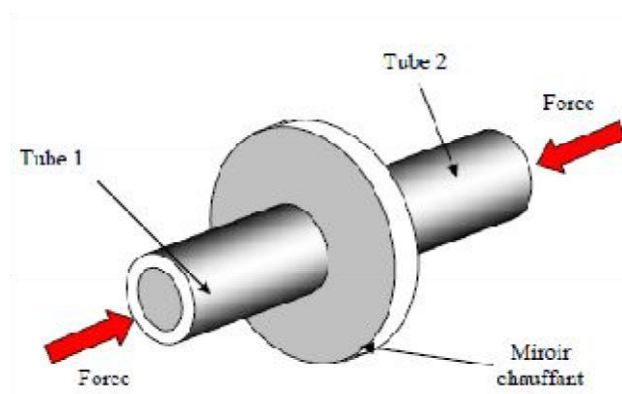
chauffage des tubes lors du soudage bout à bout
